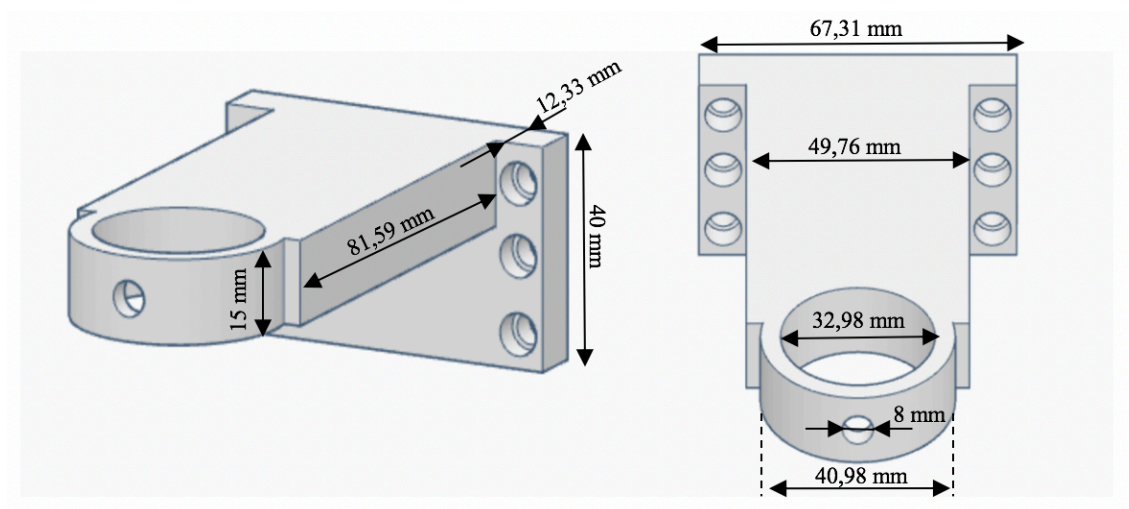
Esquema e dimensões do extensor dimensionado para acoplar o dispositivo ao posicionador.
